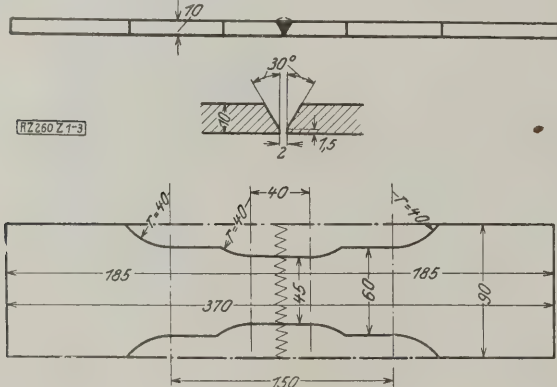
bis 3. Elektrisch geschweißter Probestab von 10 mm Dicke.
